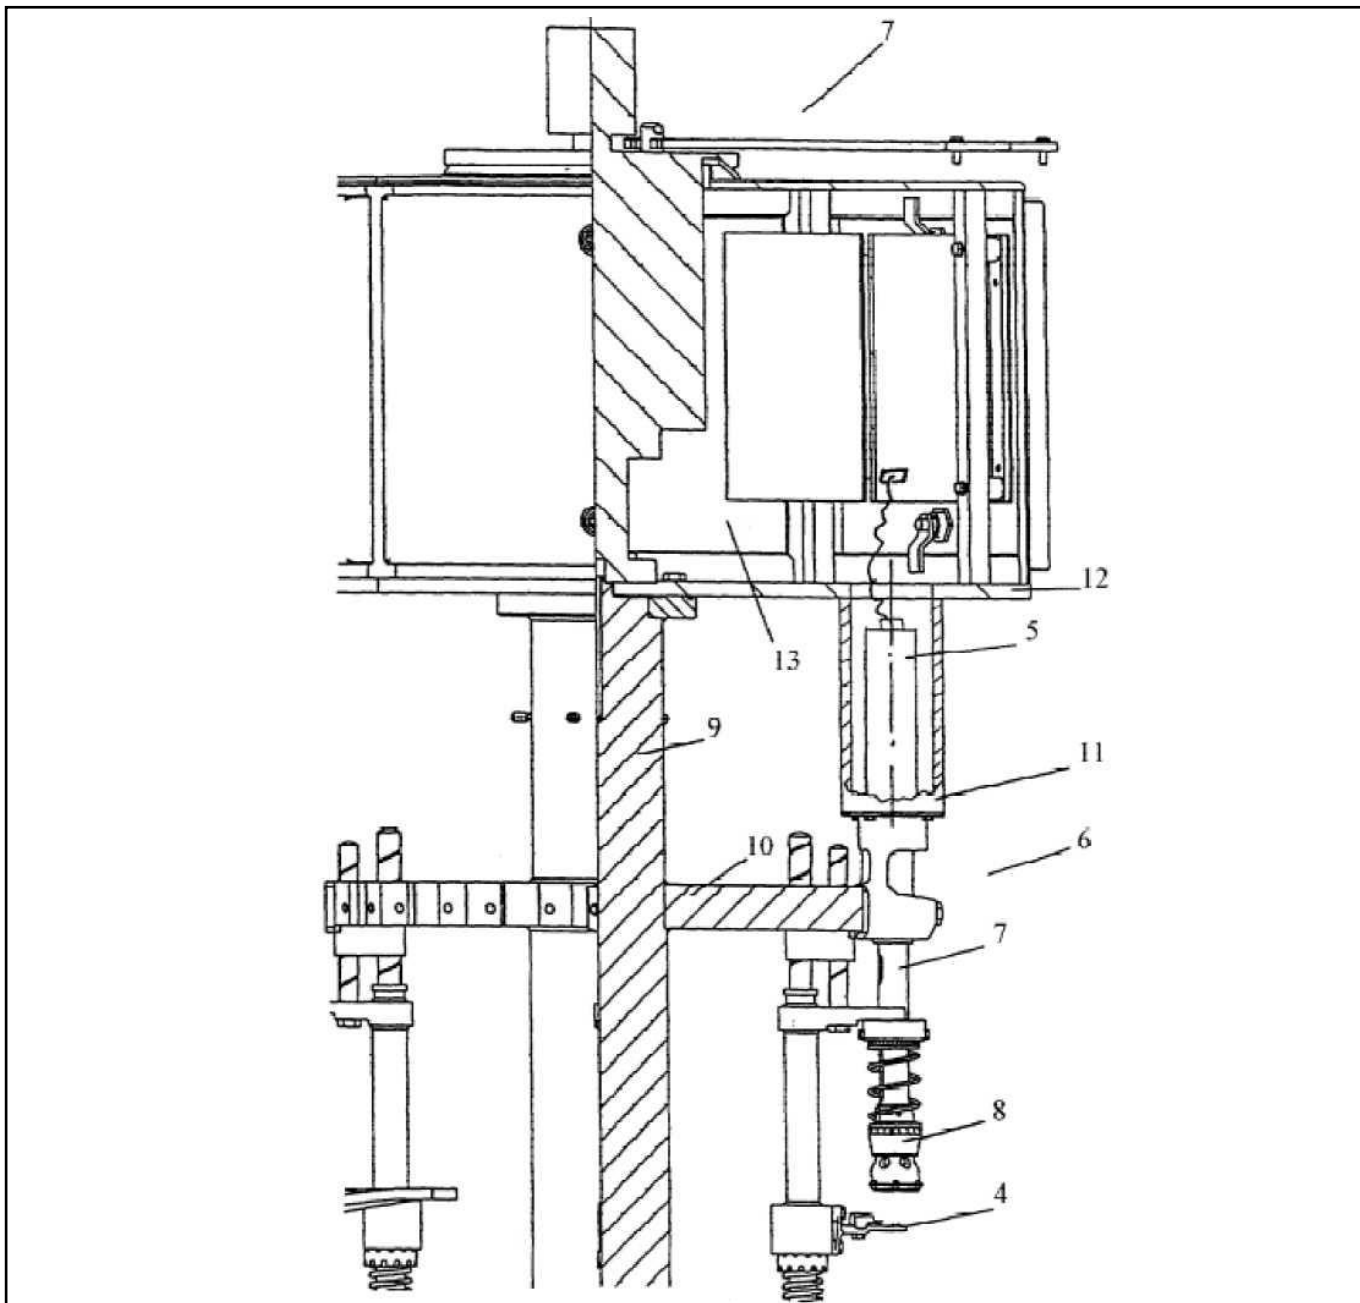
Схема закупорювальної машини для закривання пляшок
